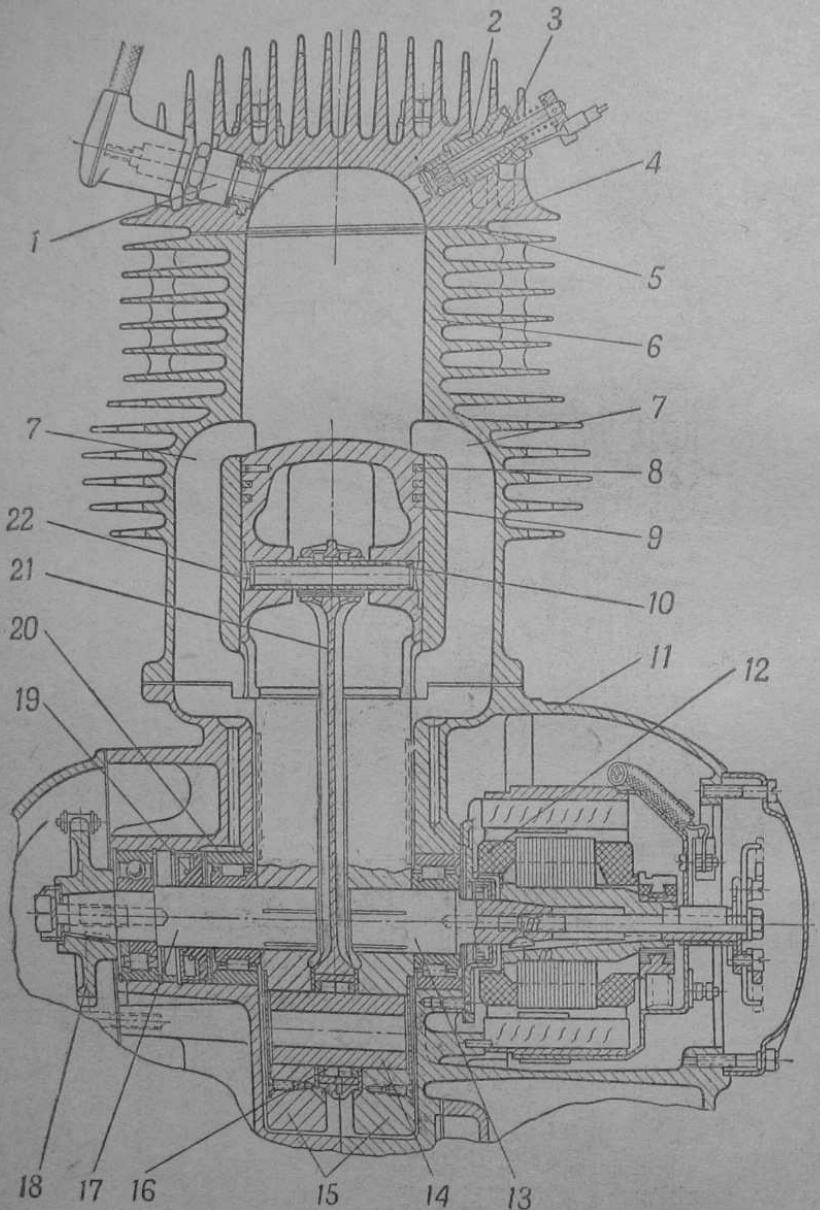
Двигатель мотоцикла ИЖ-49. Продольный разрез:
